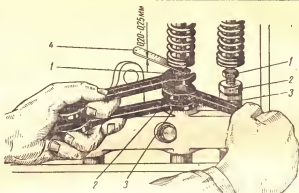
Регулировка зазора с нижним расположением клапанов:
